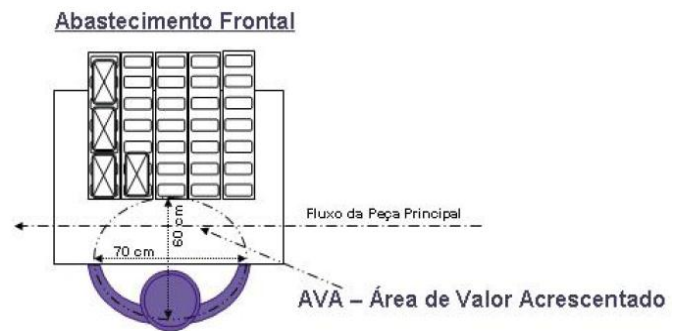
Configuração ideal de bordo de linha. Adaptado de (Coimbra 2009)
